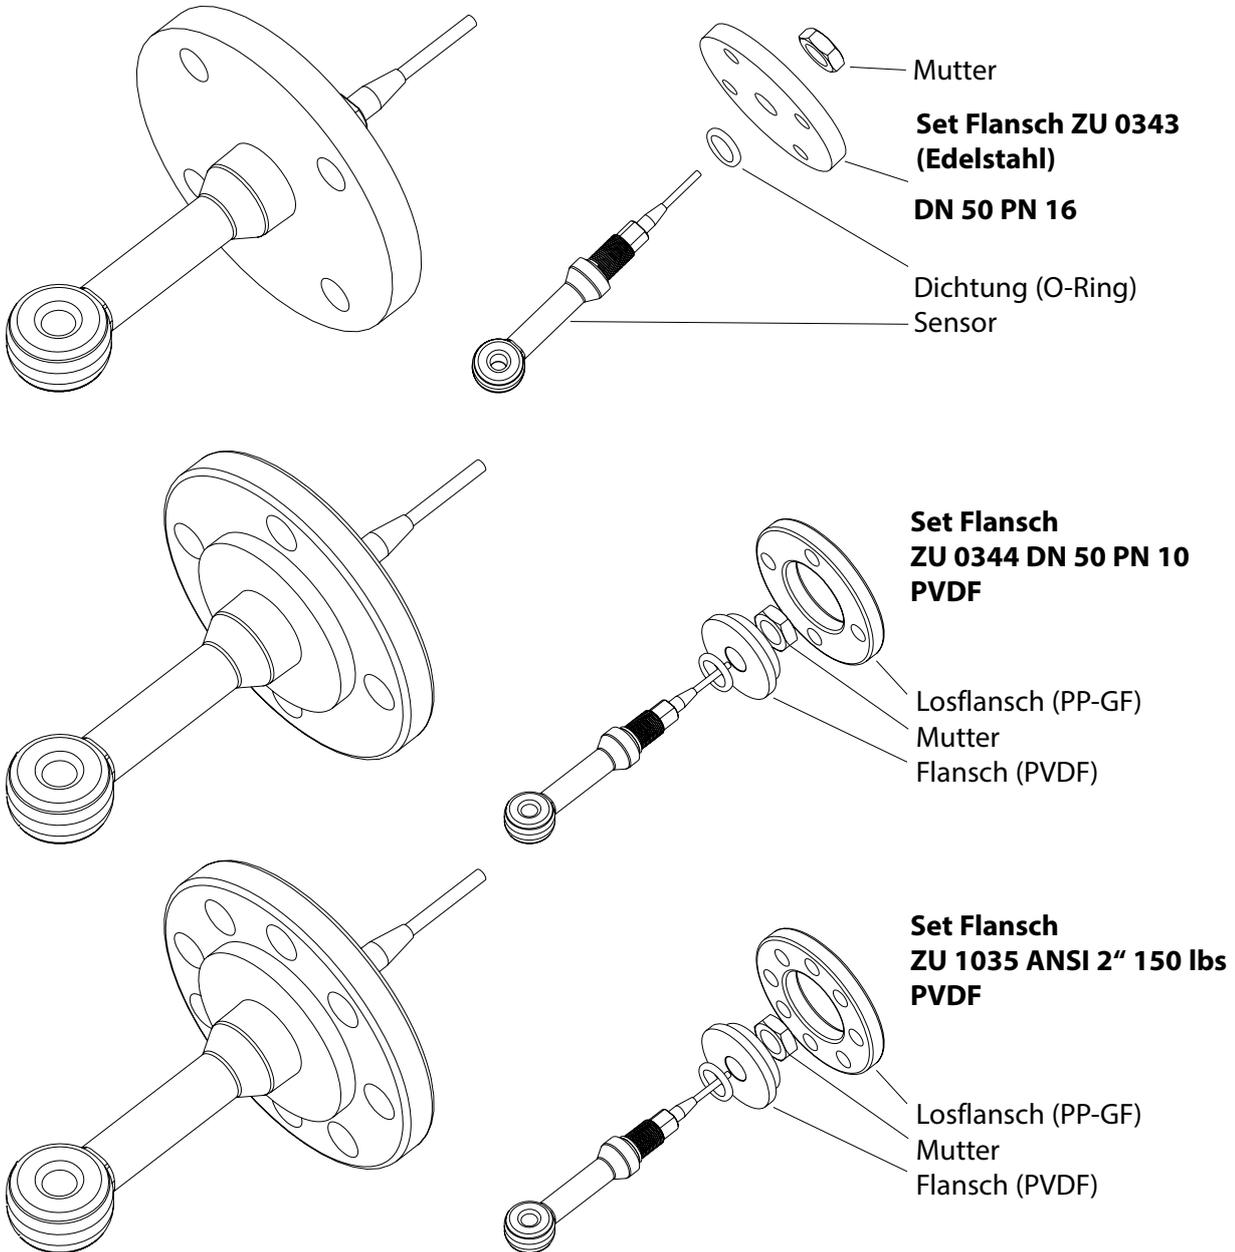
Montage Losflansch DN 50, ANSI 2"
